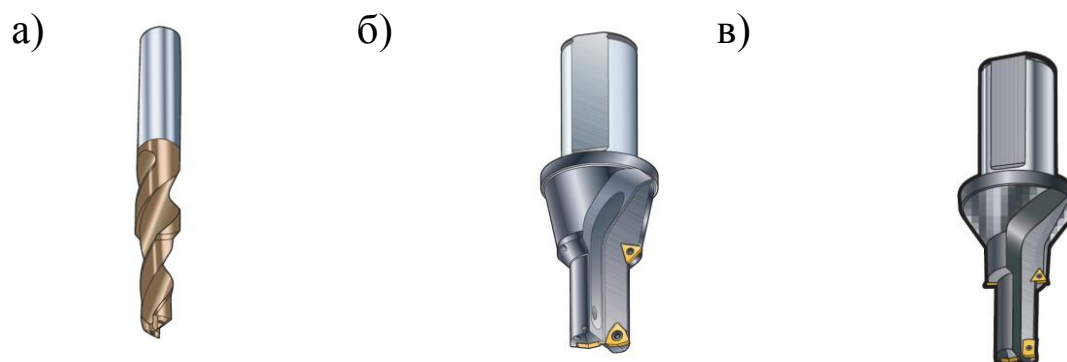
Конструктивные исполнения сверл ступенчатых: а – цельное сверло для обработки отверстия и снятия фасок; б, в – сборные сверла для обработки фасок и углублений под головку винта
